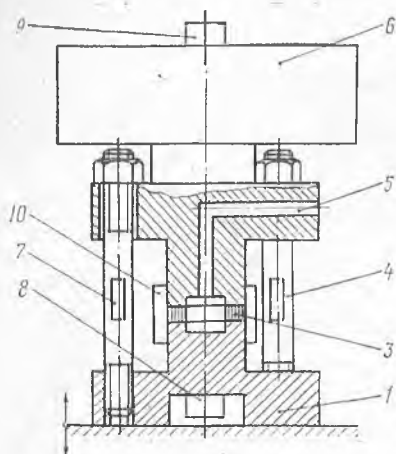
Схема установки для вибрационных испытаний соединений трубопроводов:
